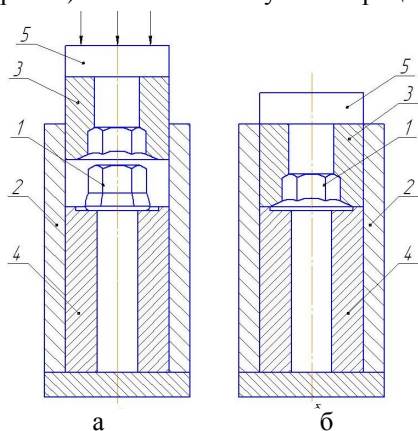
Схема высадки фланца болта: а – начальный этап высадки; б – конечный этап: 1 – заготовка; 2 – стакан; 3 – пуансон; 4 – матрица; 5 – упор
